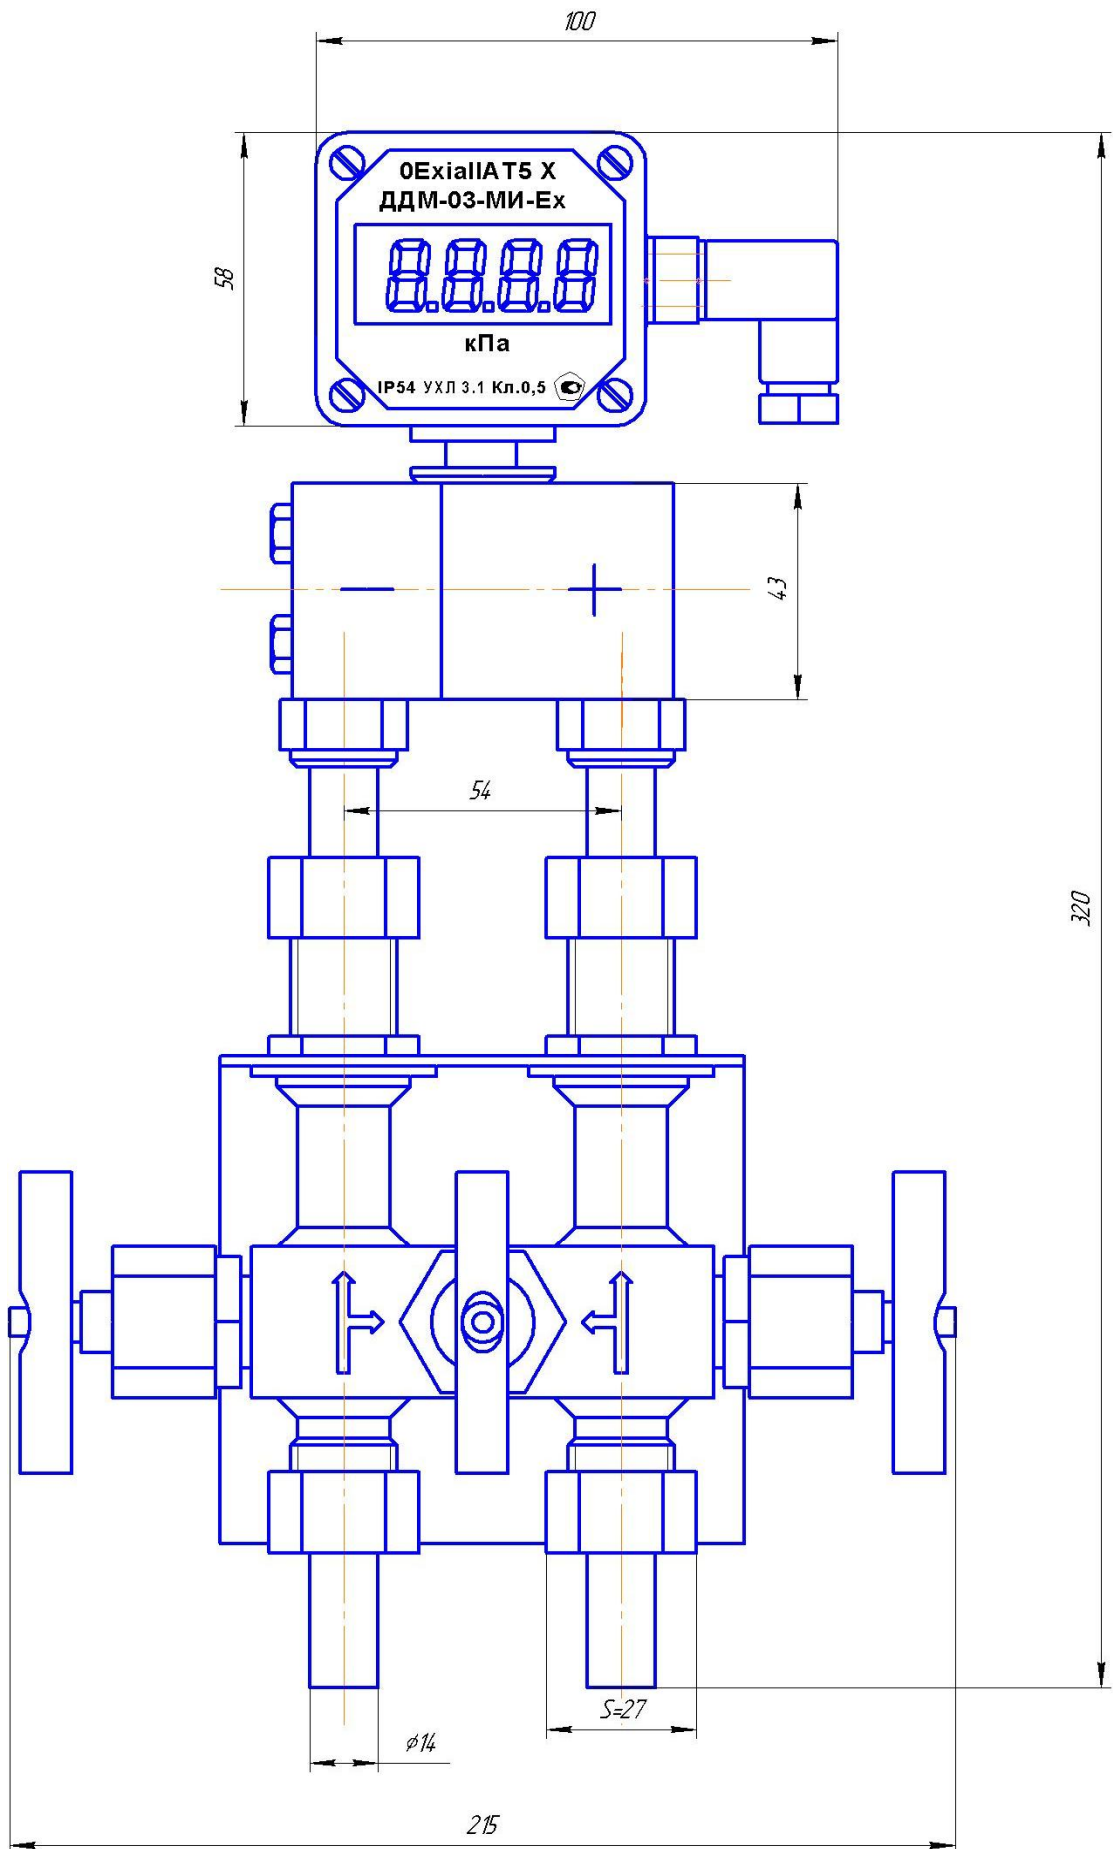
Габаритные и присоединительные размеры датчика ДДМ-03-ДД-МИ; ДДМ-03-ДД-МИ-Ех с вентильным блоком.
